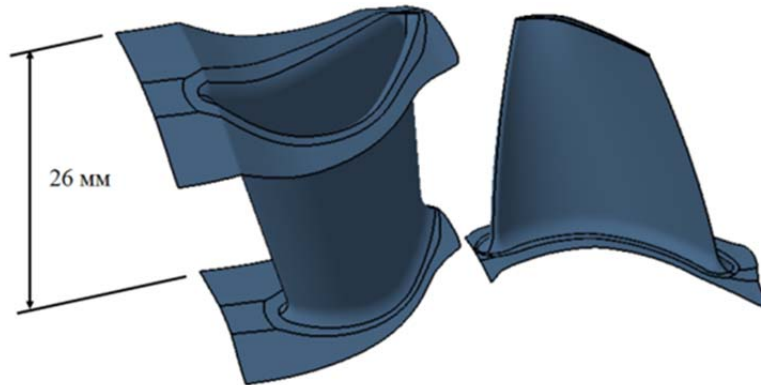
Сопловая и рабочая лопатки турбины компрессора
